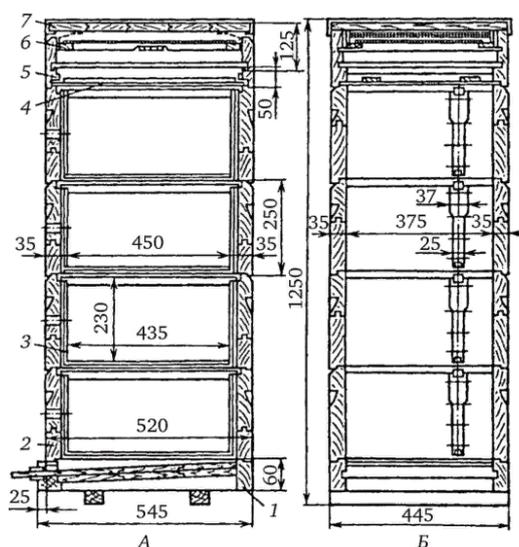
Многокорпусный улей: А, Б – продольный и поперечный разрезы (размеры даны в миллиметрах); 1 – дно; 2 – корпус; 3 – рамка; 4 – потолок; 5 – подкрышник; 6 – вентиляционная рама; 7 – крыша
